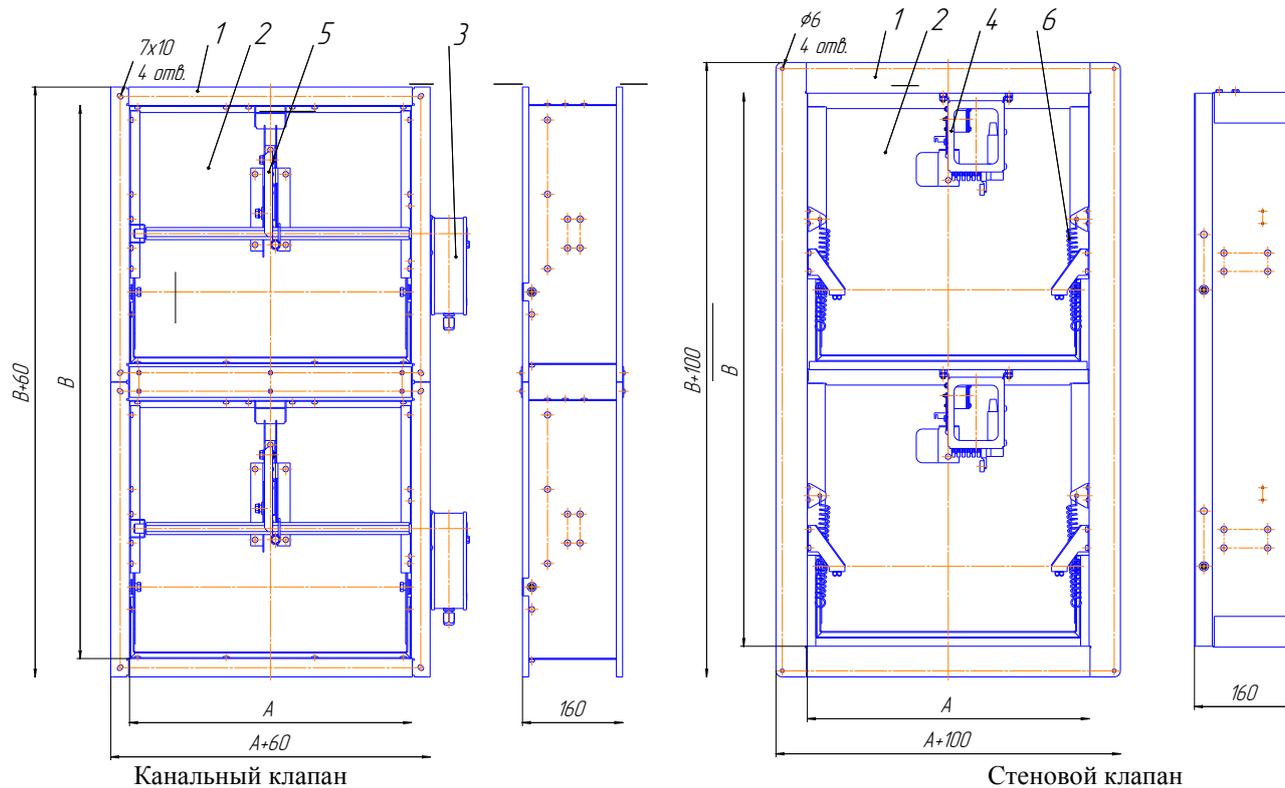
Общий вид исполнительного механизма с магнитом и места регулировок
